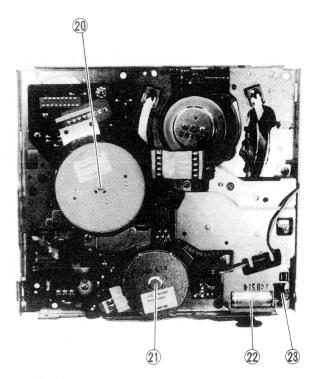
Unteransicht / Bottom view
